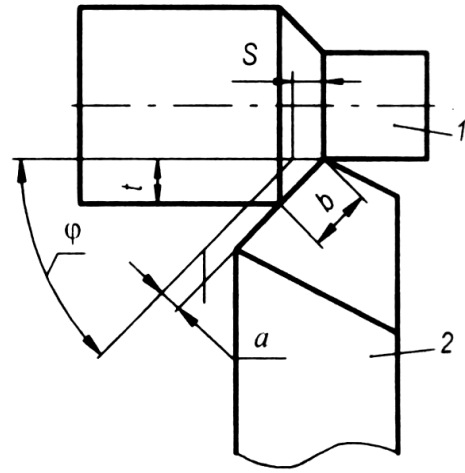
Площа зрізуваного шару: 1 — заготовка; 2 — різець; a - товщина зрізуваного шару; b - ширина зрізуваного шару; S - подача; t - глибина різання; φ — головний кут у плані
